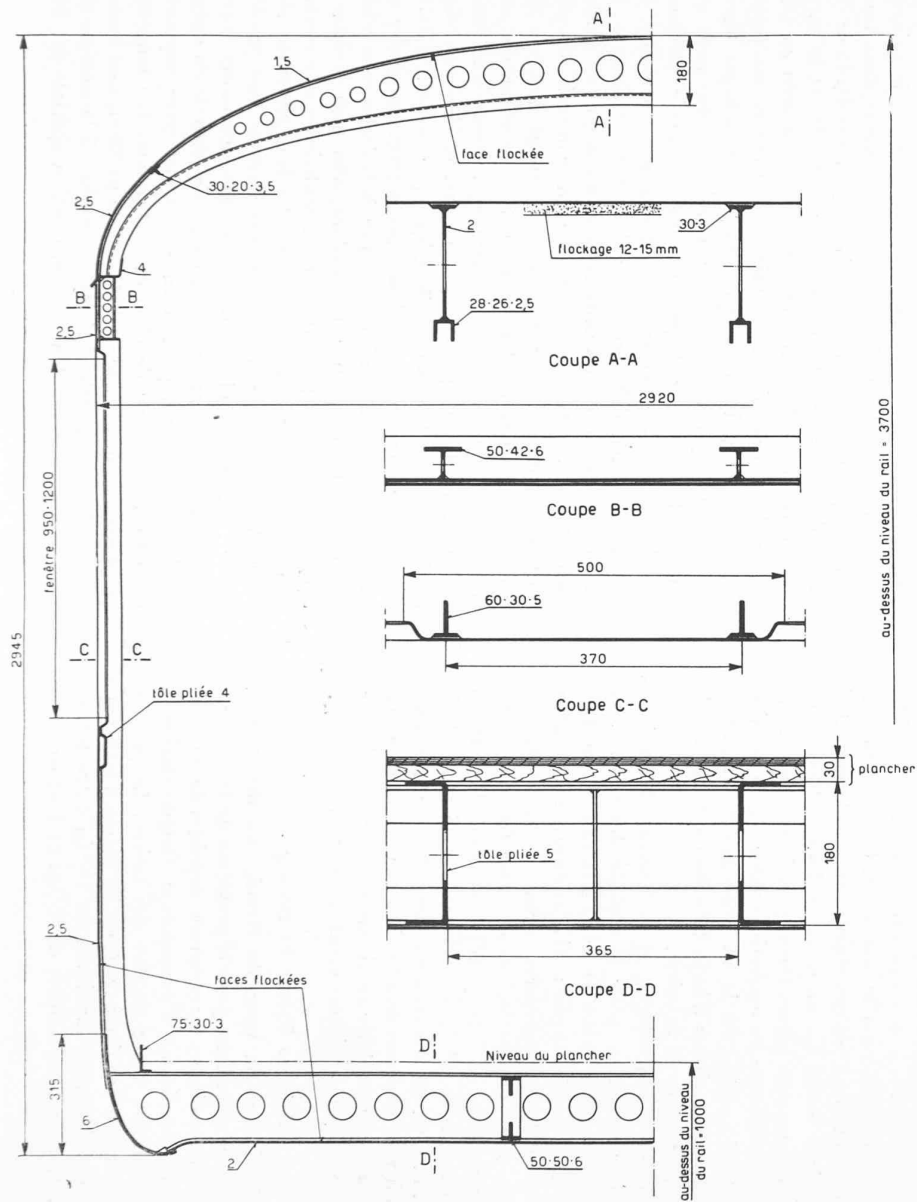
Demi-coupe transversale de l'ossature du châssis-caisse d'une voiture légère en acier.
